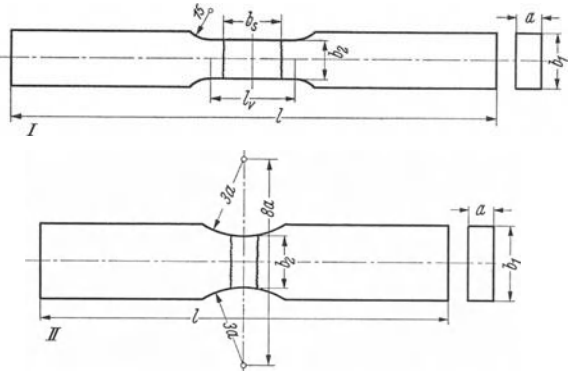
Schweißflachstäbe für den Zugversuch.
